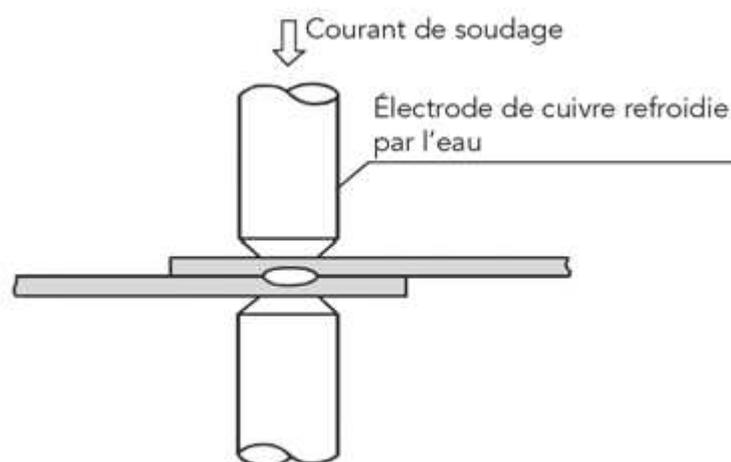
Principe du soudage électrique par résistance par points.
